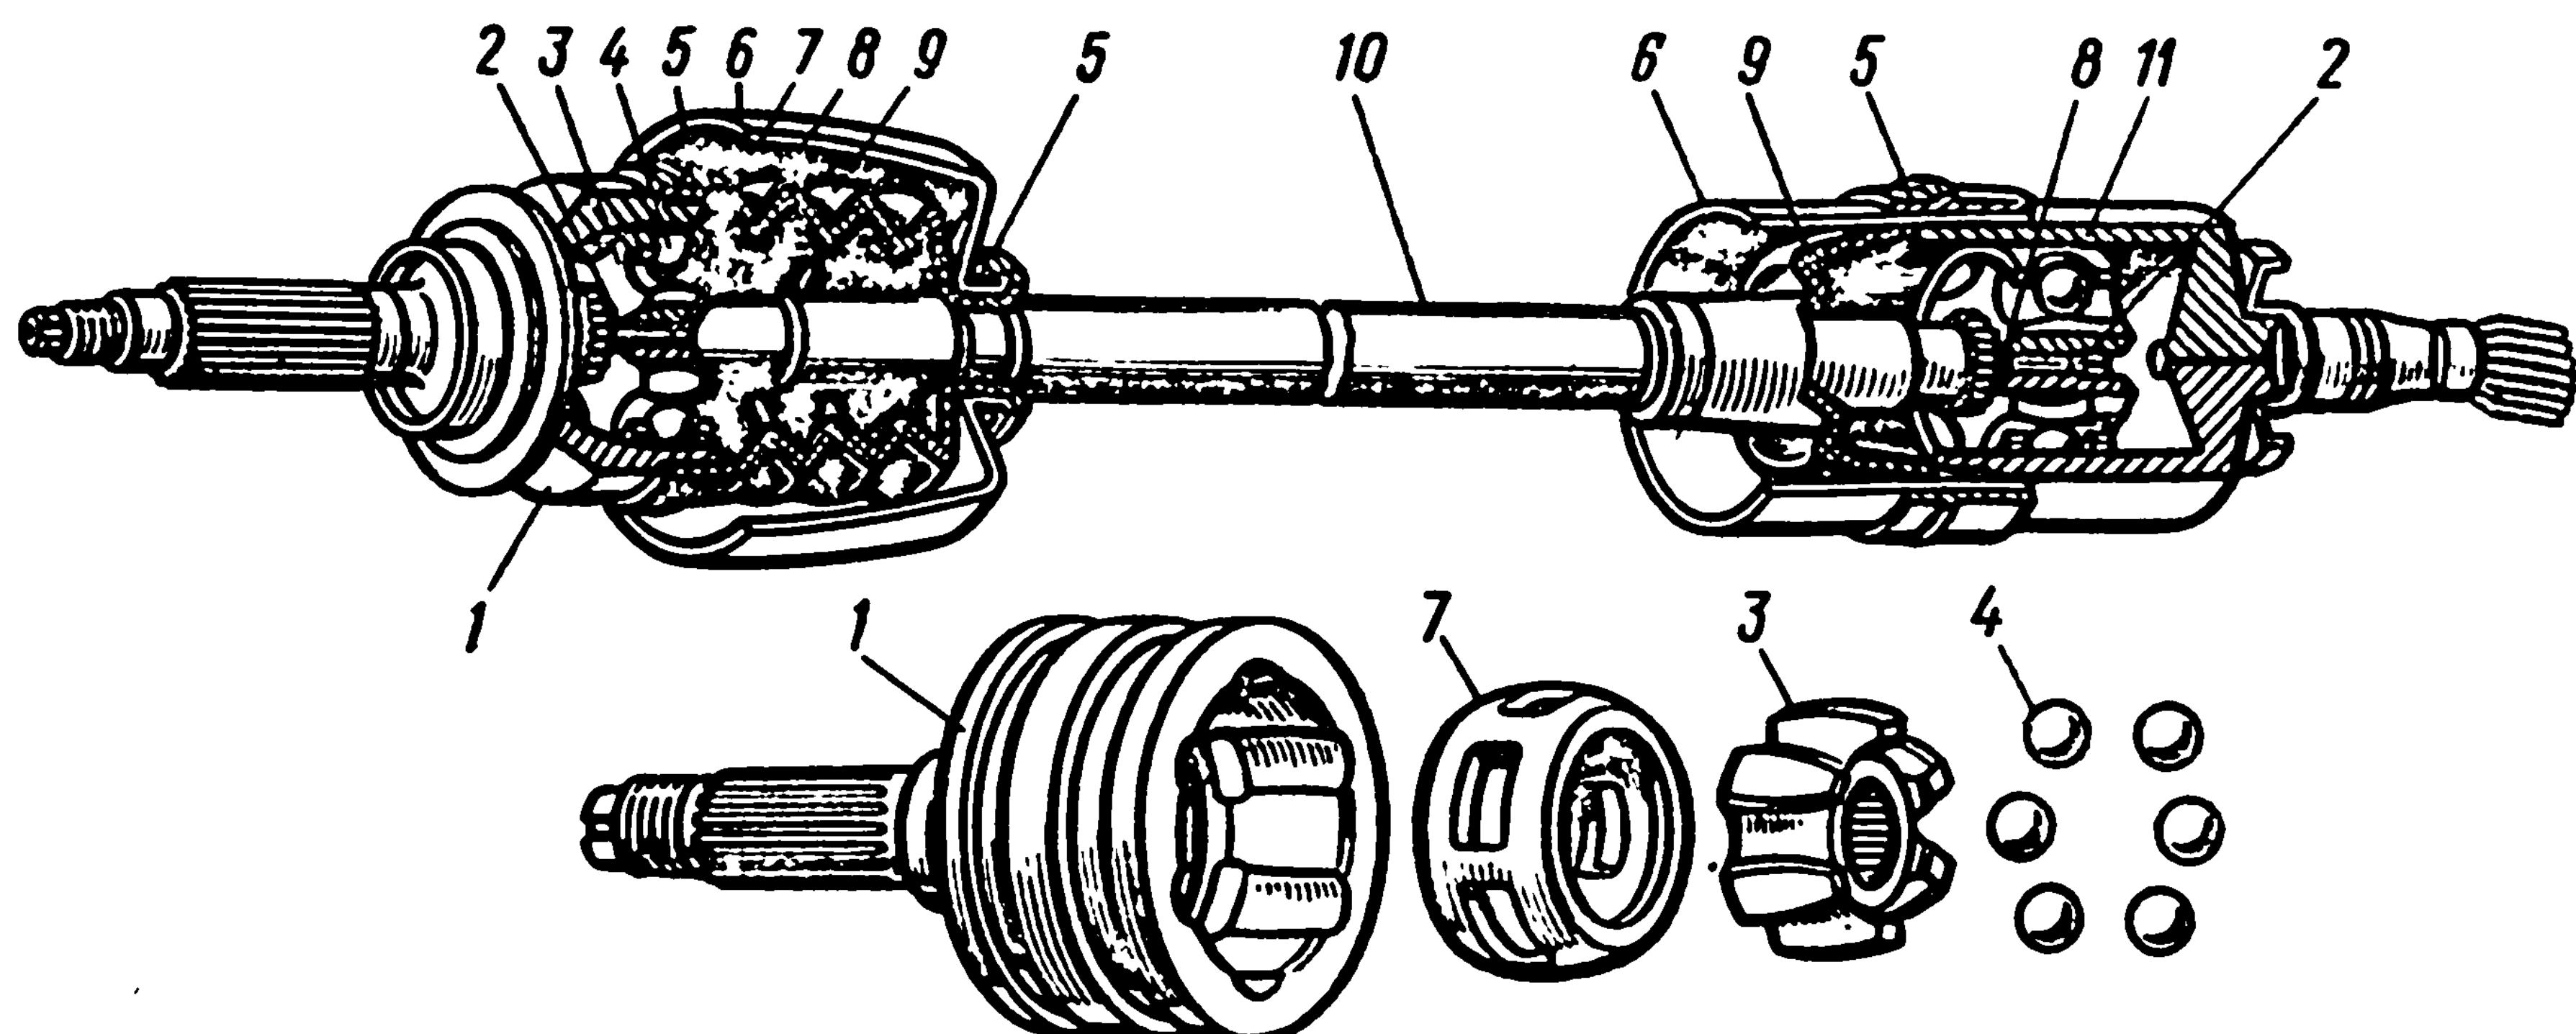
Привод передних колес автомобиля ВАЗ-2121
